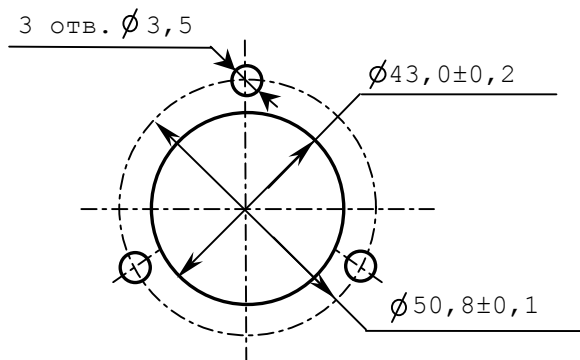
Установочные размеры штурвала ZBG-5-003-100
